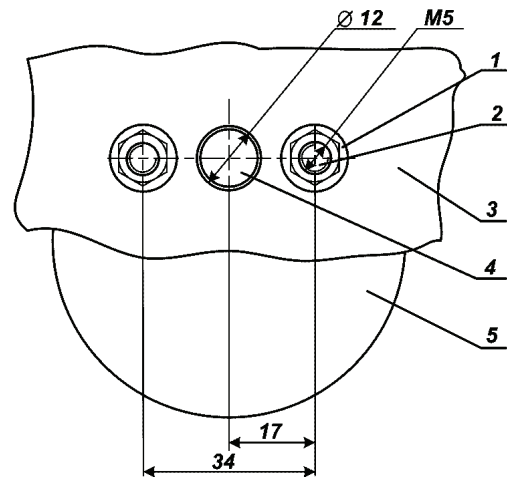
Установка УБОП на неподвижной части привода электрооборудования: 1 – гайка М5 с шайбой, 2 – винты М5, 3 – неподвижная часть привода, 4 – шток, 5 – корпус УБОП
